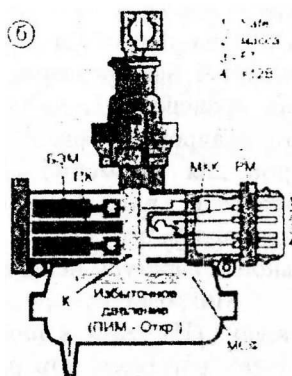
Пневмоприводной исполнительный механизм замка двери
